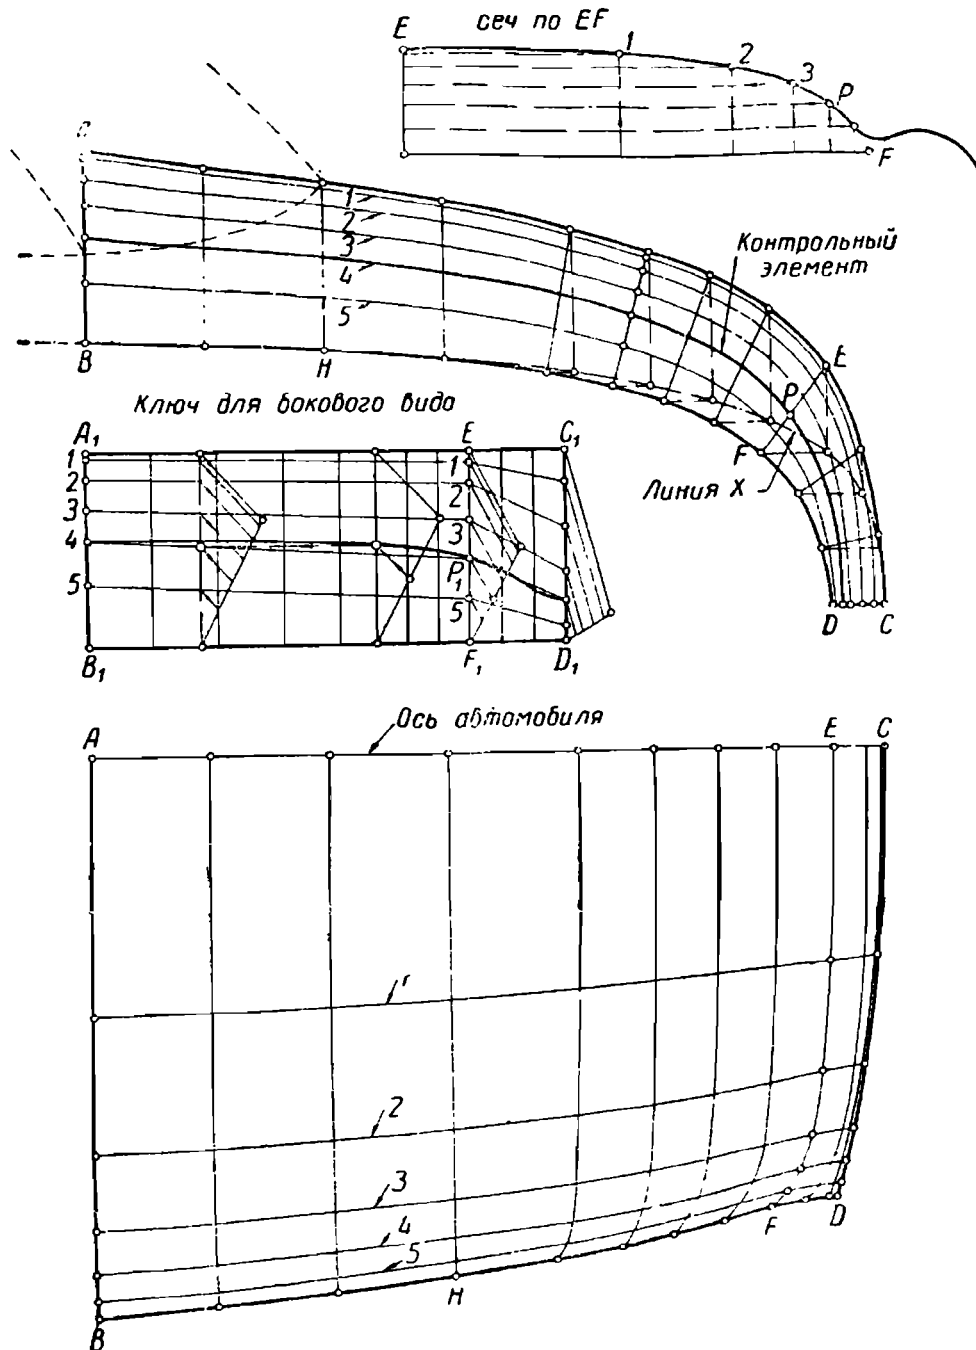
Разбивка поверхности кабины грузового автомобиля.
